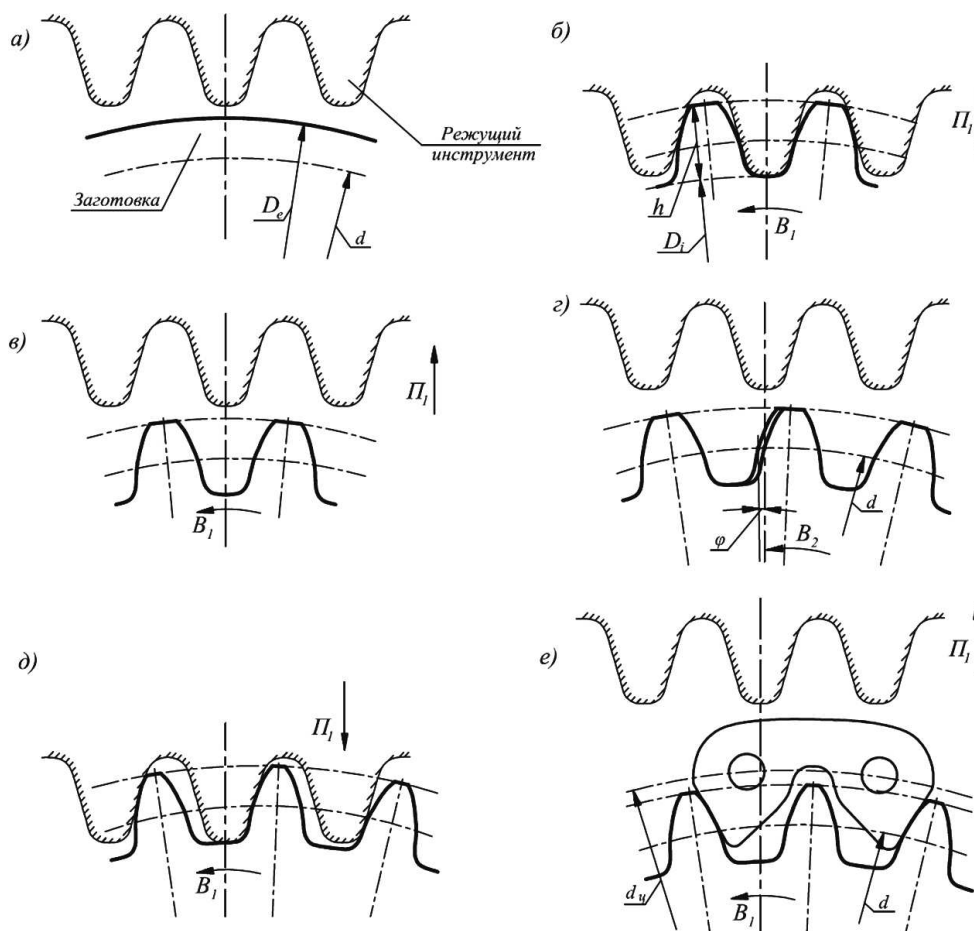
Этапы нарезания зубьев эвольвентной звездочки стандартным режущим инструментом:
